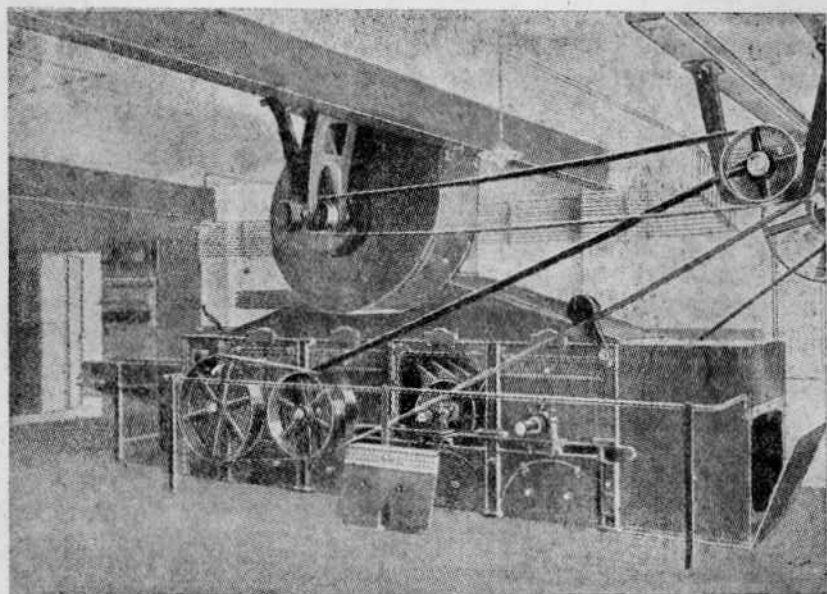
Дрешер. Над машиной помещен вентилятор для отсоса пыли
